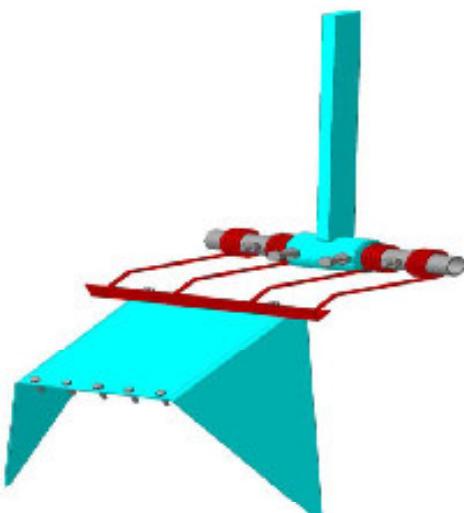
Профилеформователь узкопрофильных гряд для установки на агрегат универсальный АУ-М2 (3D модель)
